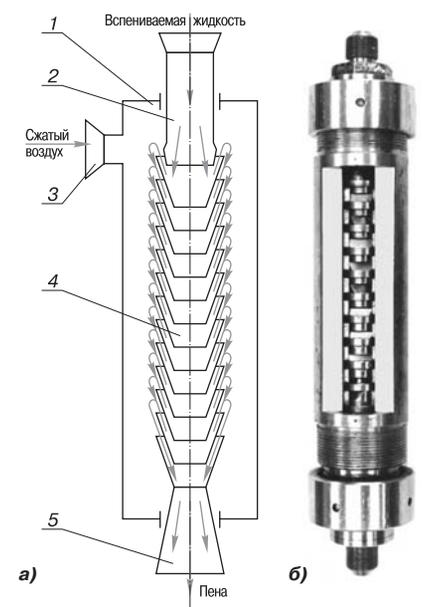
Многоконусный струйный пеногенератор: а – схема; б – внешний вид
